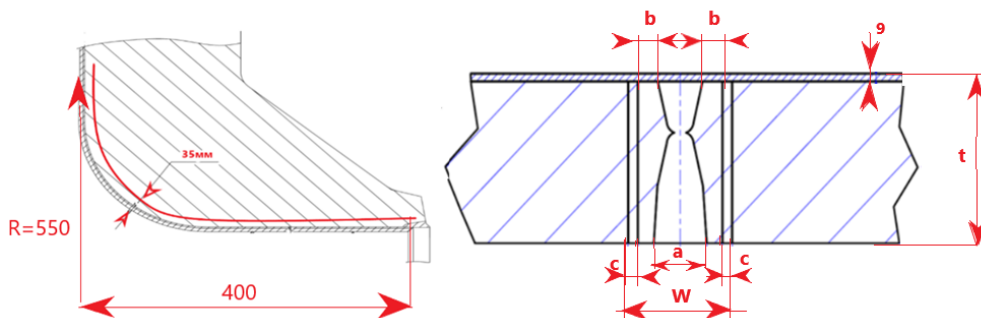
Зона контроля сварных соединений корпуса реактора и радиусных переходов
